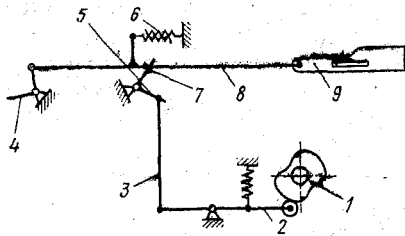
Схема центральной уточной вилочки станка АТ-2-175-Ш
